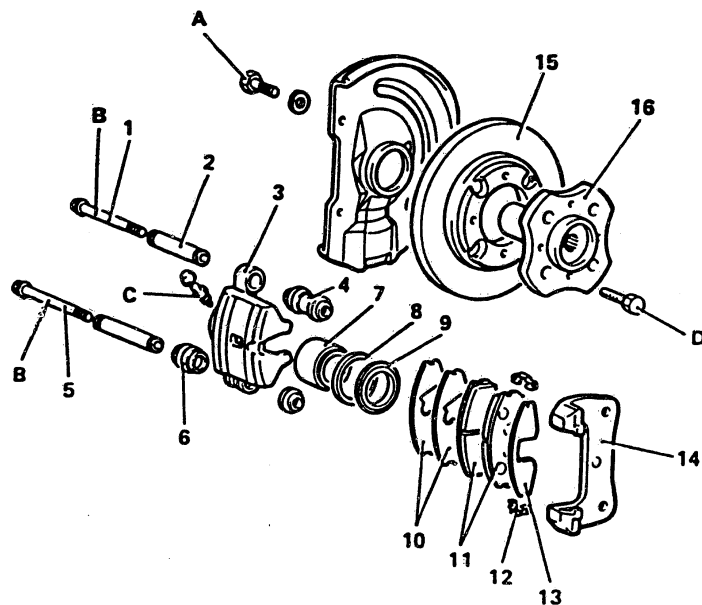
Einzelteile der Scheibenbremsen vorne: 1 Führungsbolzen B - 2 Büchse - 3 Bremssattel - 4 Stiftmanschette - 5 Führungsbolzen A - 6 Manschette - 7 Kolben - 8 Kolbendichtring - 9 Staubmanschette - 10 Inneres Antiquitschblech - 11 Bremsbelag - 12 Führungsstück - 13 Äusseres Antiquitschblech - 14 Ankerplatte - 15 Bremsscheibe - 16 Radnabe.
